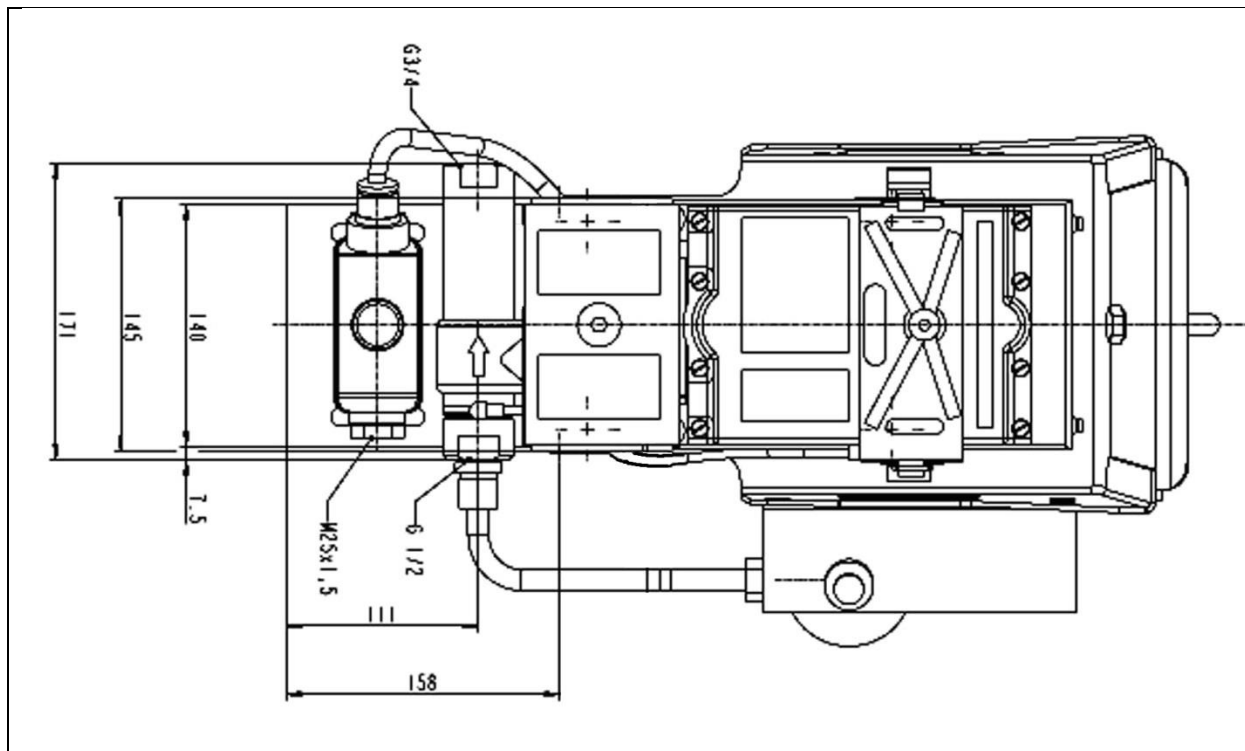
Mechanische Abmessungen des VN115/87plus: Draufsicht
